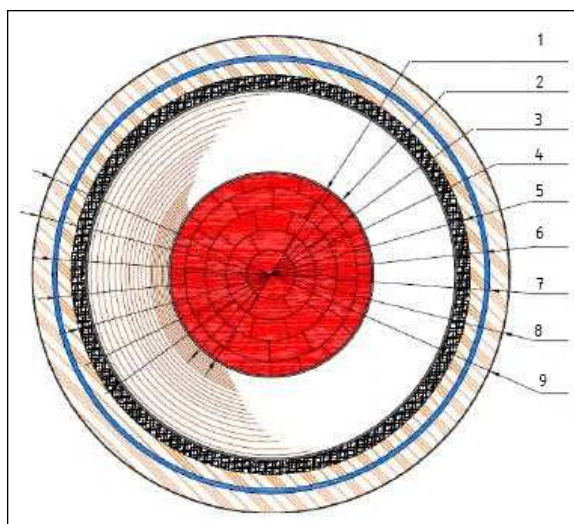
Sezione tipica del cavo di potenza terrestre
